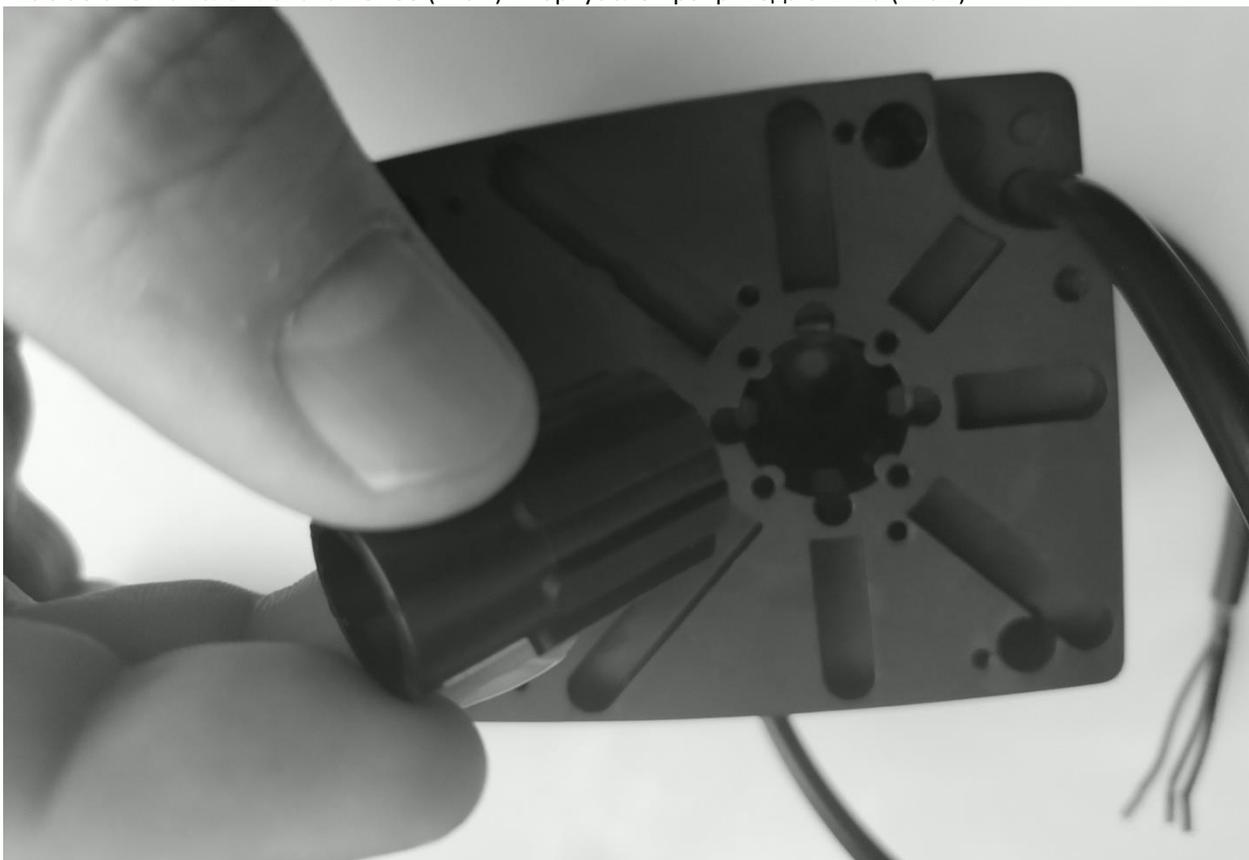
Подготовка монтажа адаптера клапана КСТ 46 (Рис.2) на корпус электропривода ЭПК 1а (Рис.1)
